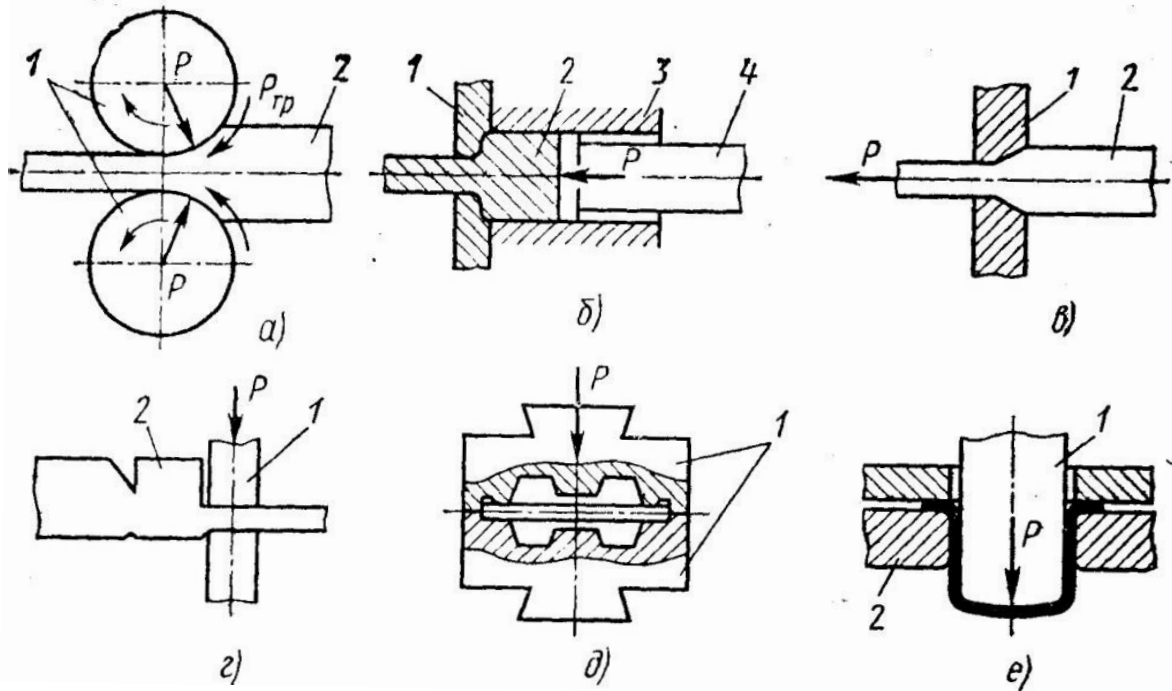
Схеми основних видів обробки металів тиском
